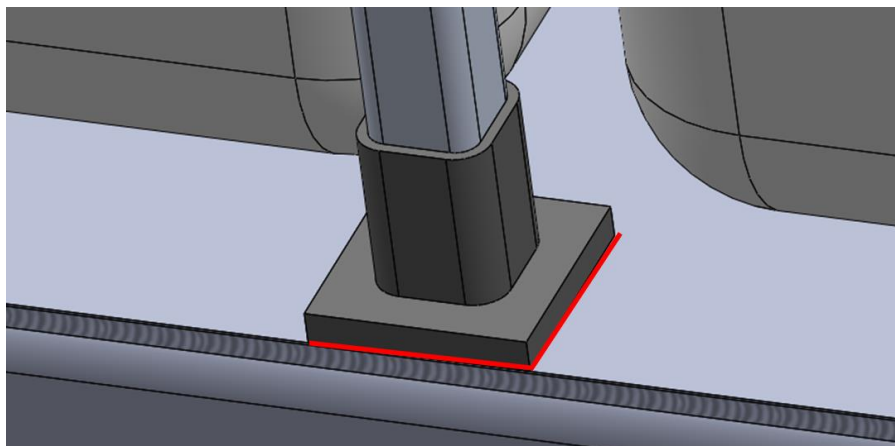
Representación de la soldadura de la unión ANCLAJE BARRERAS-CHASIS [fuente propia]
